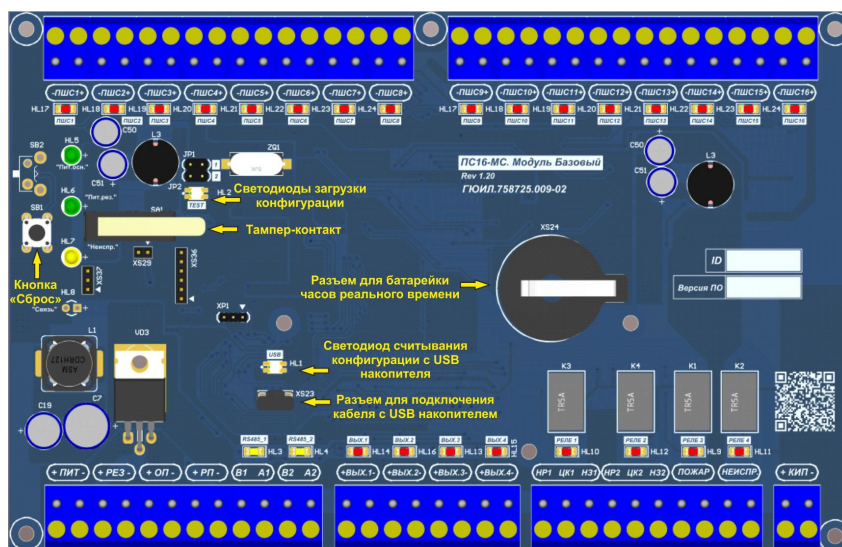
Внешний вид базовой платы «PC16-МС»
